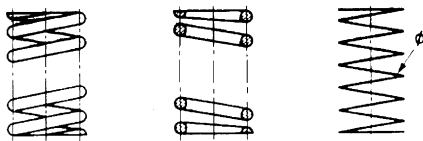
Zylindrische Schraubendruckfeder aus Draht mit rundem Querschnitt (DIN 2089, DIN 2095, DIN 2096)
